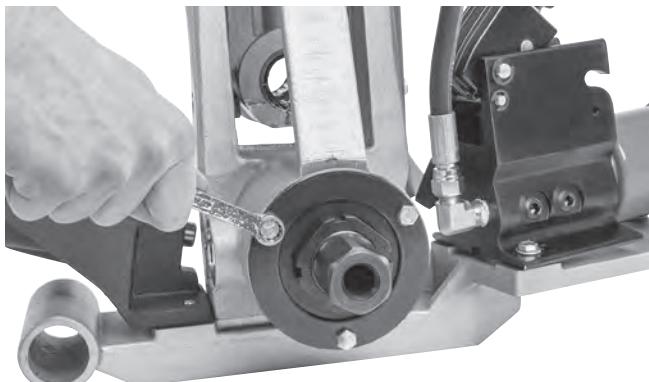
Ausbauen der Sechskantschrauben für die Halteplatte
